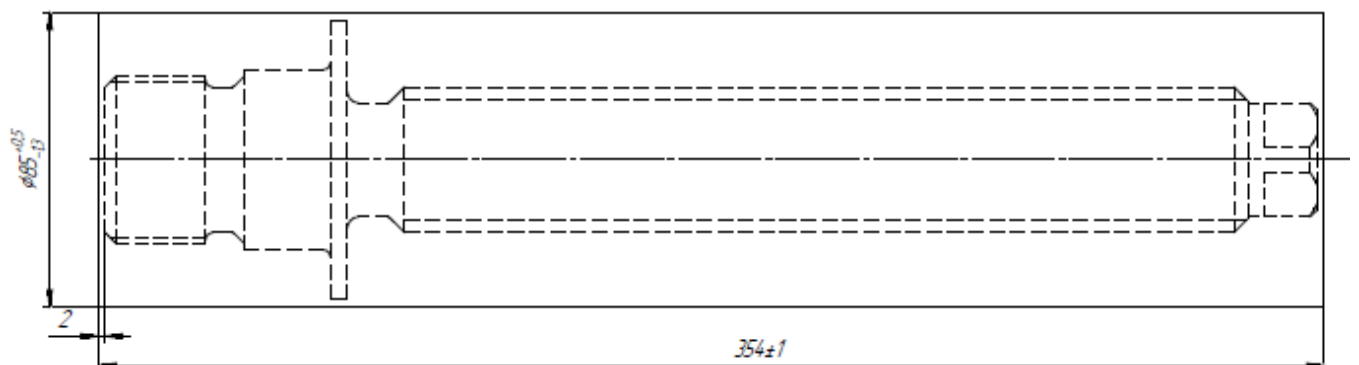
Ескіз заготовки з прокату ДСТУ 4738:2007
